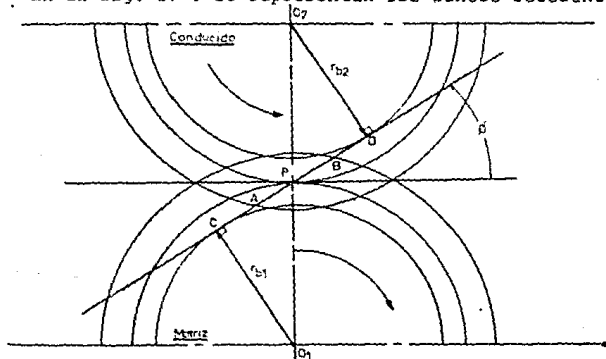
Longitud de contacto entre dos engranes engranados
